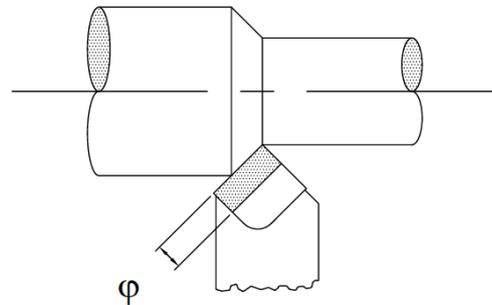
Нейтральный угол при вершине для строгания и черновой обработки
